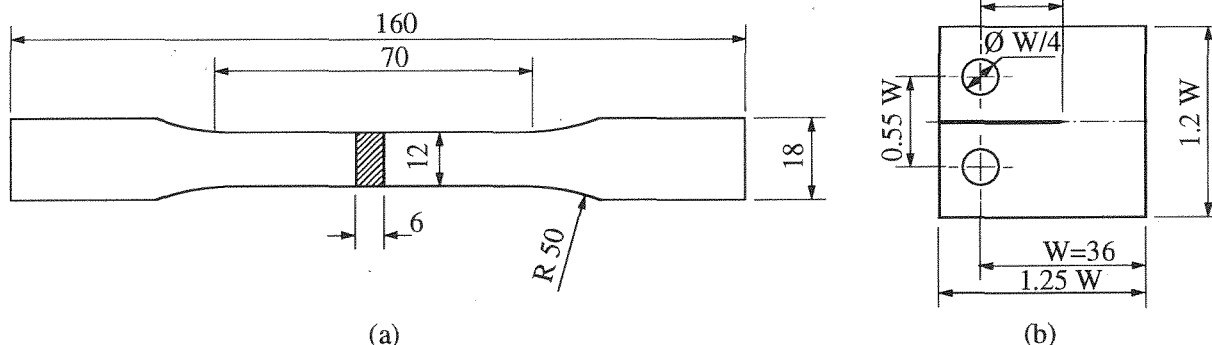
Geometria dos provetes (dimensões em mm): a) ensaios de tracção; b) ensaios de tenacidade à fractura
